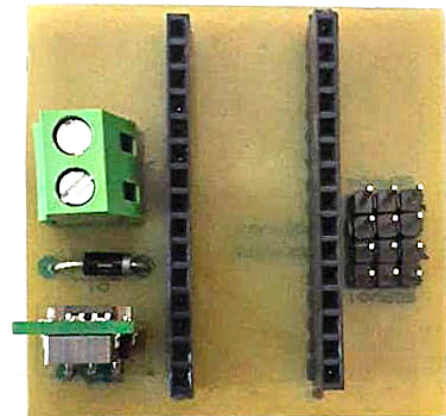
Sosa, G. 2023. Diseño final de placa PCB realizado con la ayuda de Juan Galarza.
